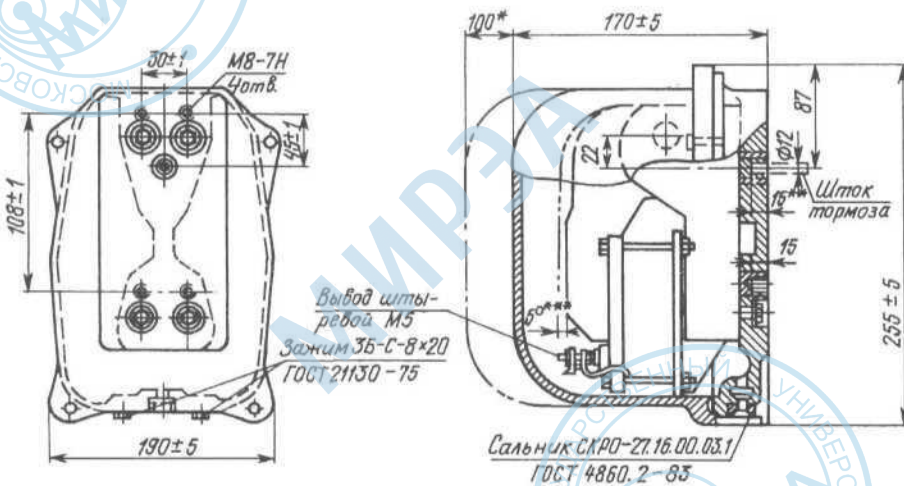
Габаритные и установочные размеры электромагнита типа MOM-110
